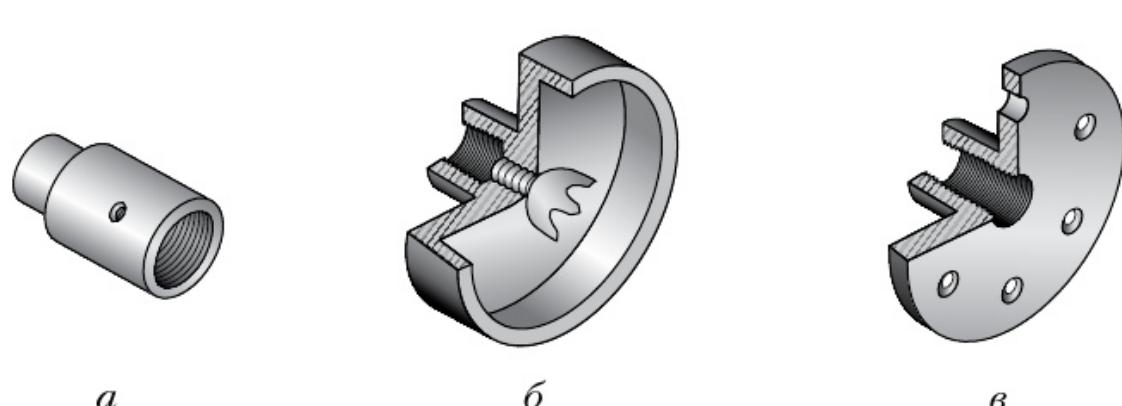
Приспособления для закрепления заготовок: а – патрон; б – трезубец; в – планшайба
